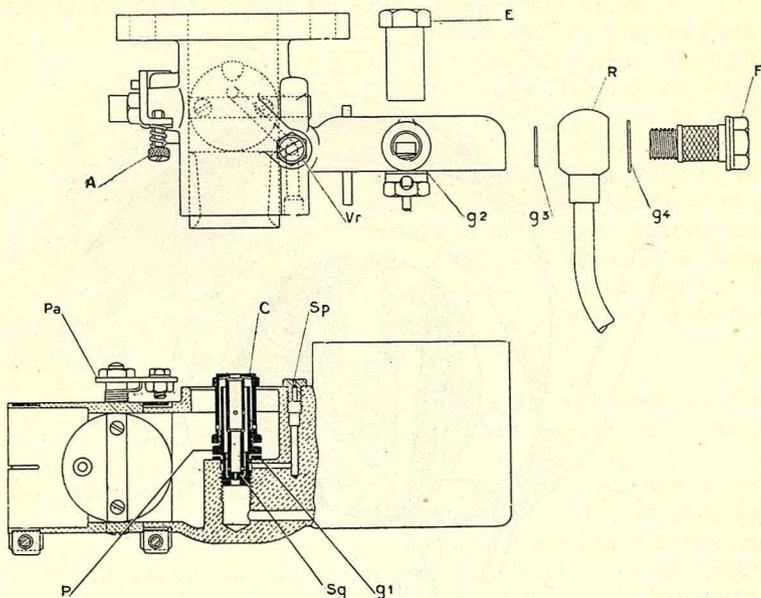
Carburateur Solex M.O.V.T. 40.
